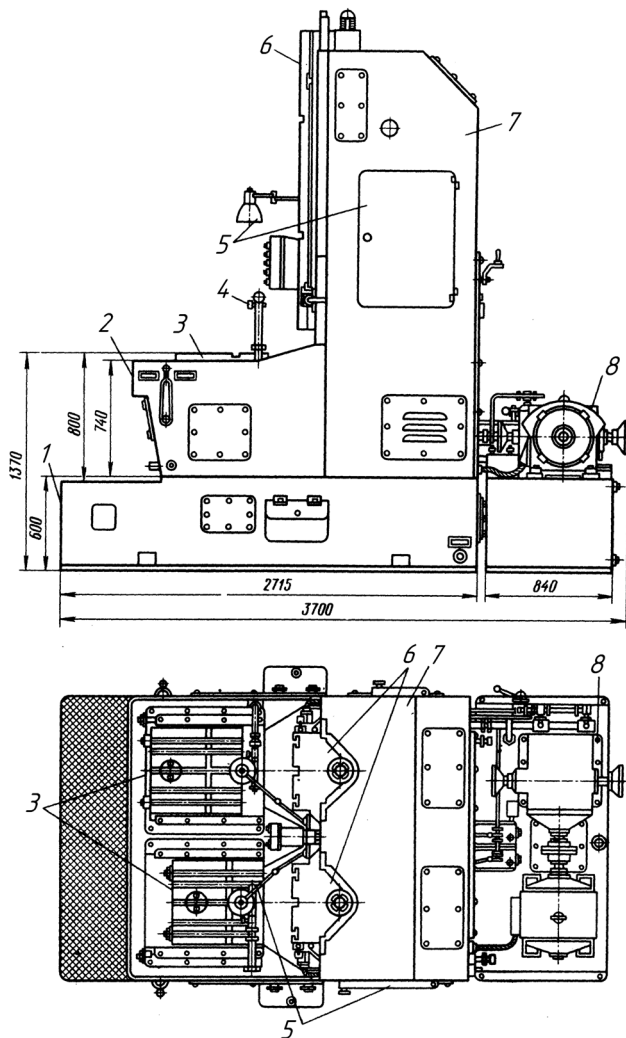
Вертикально-протяжной двоянный станок 7Б76Д для наружного протягивания
